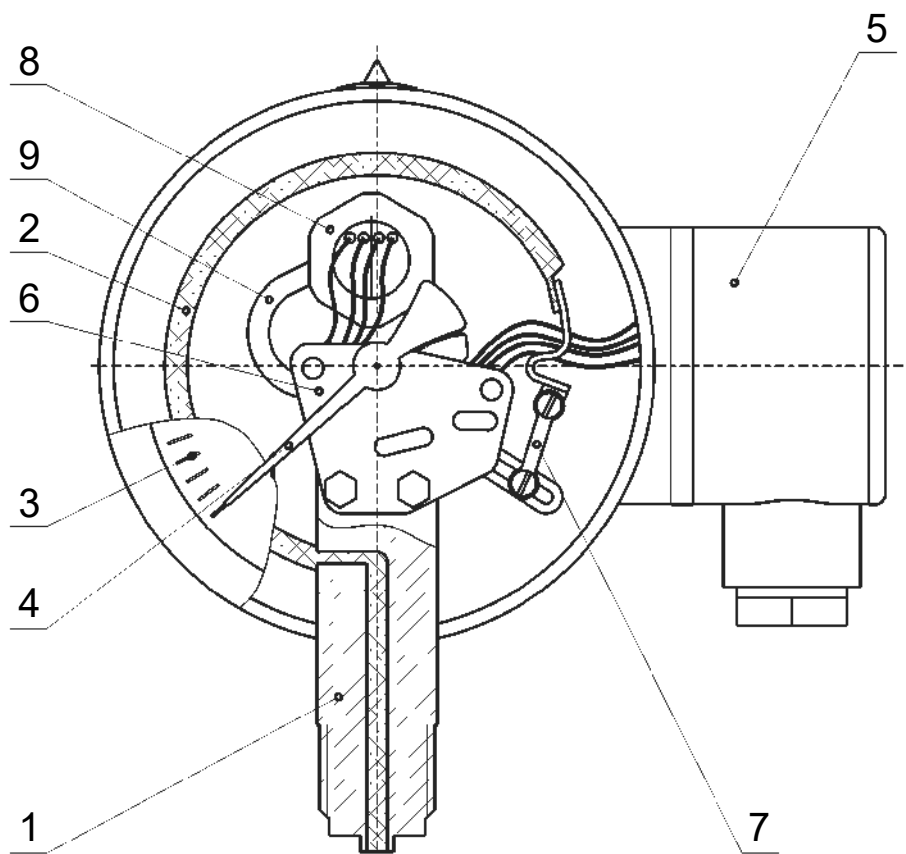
Устройство манометра ТМС. 1 – штуцер; 2 – трубка Бурдона; 3 – циферблат; 4 – стрелка; 5 – кабельный разъем; 6 – трибко-секторный механизм; 7 – тяга сектора; 8 – корпус преобразователя; 9 – трубопровод подачи среды к преобразователю.
